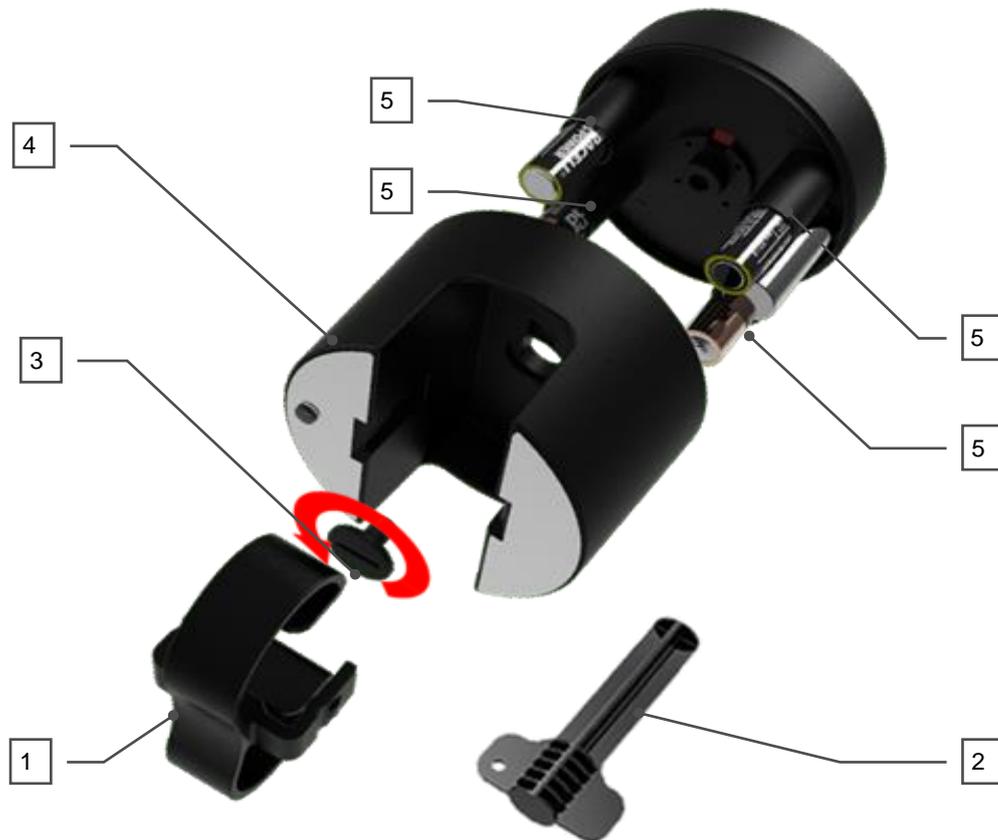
Geöffnete Ansicht LE CYLINDER
